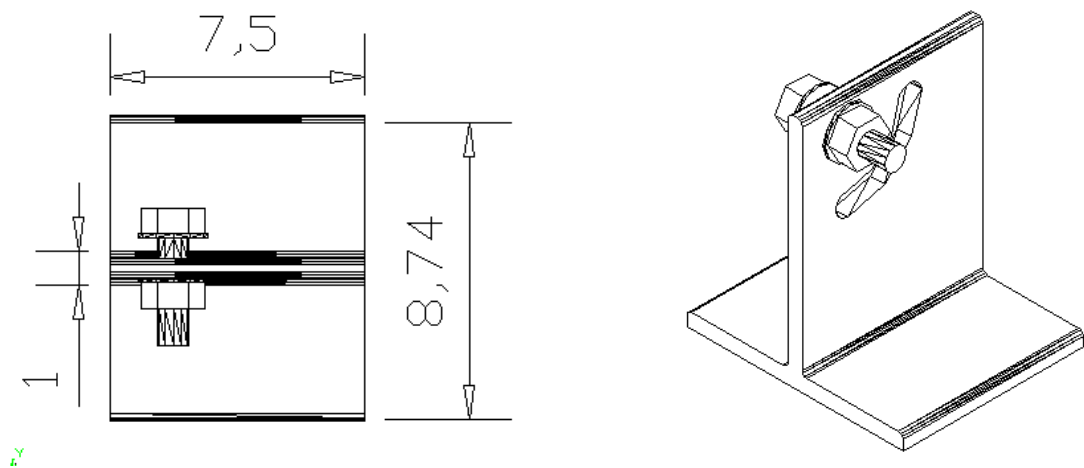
Vista y Dibujo de conjunto de Pieza que sujeta el otro extremo del alternador
